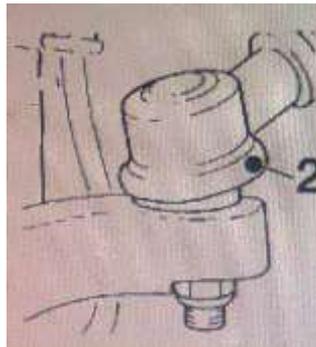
Montaje de Terminal de Dirección en la Masa
